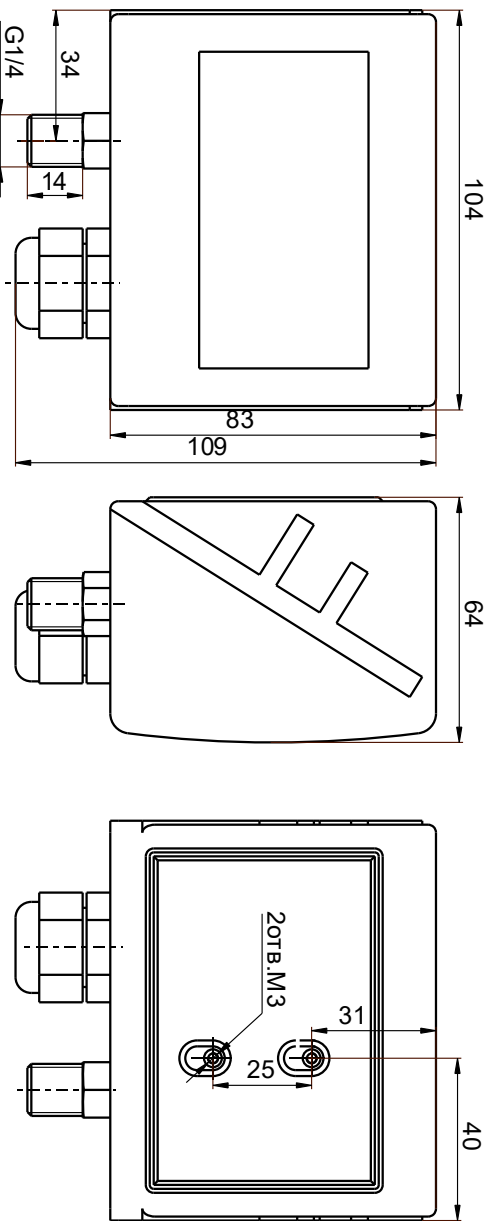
Габаритные и присоединительные размеры РД-2Р (G1/4, модель 35) в корпусе IP55
